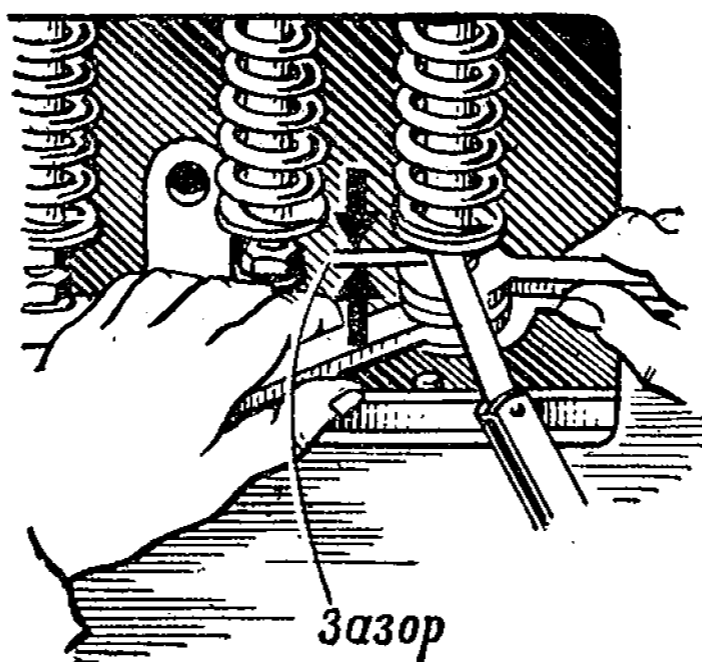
Регулировка зазора между регулировочным болтом толкателя и стержнем клапана
